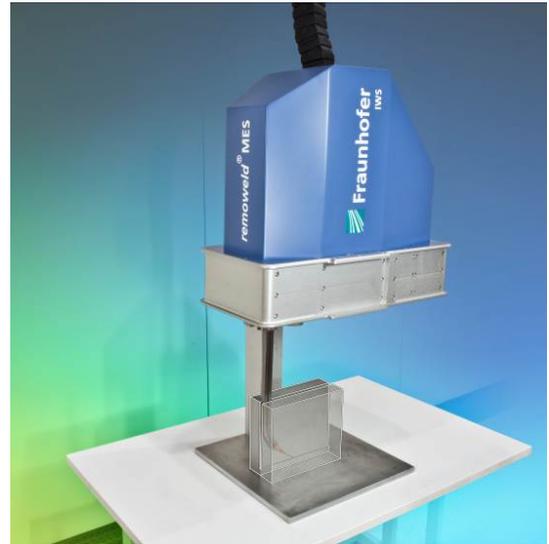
Modular aufgebauter remoweld®MES-Schweißkopf
